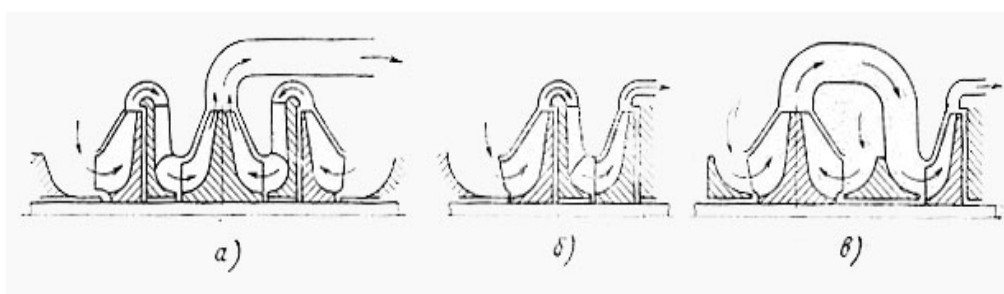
Схемы двухступенчатых центробежных компрессоров:
